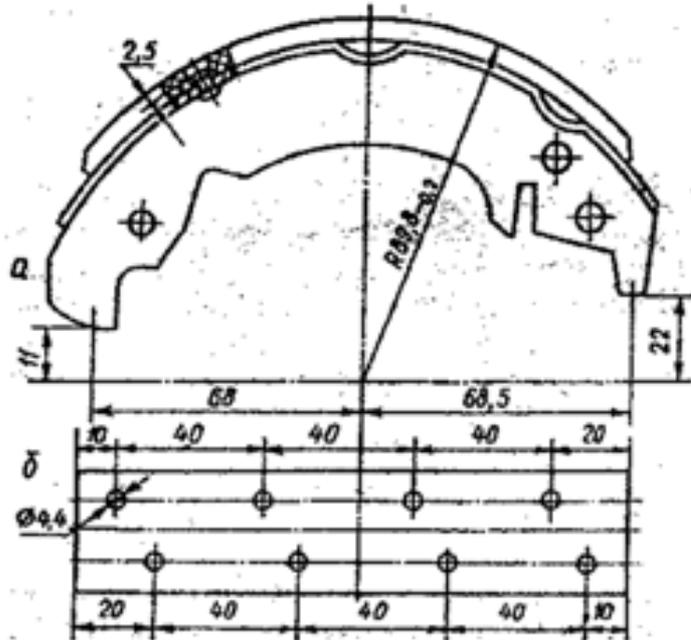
Крепление фрикционных накладок тормоза заклепками: а - колодка тормоза в сборе; б - фрикционная накладка в развертке (размеры 2,5 и 89,8 - 0,2 указаны после шлифовки).
